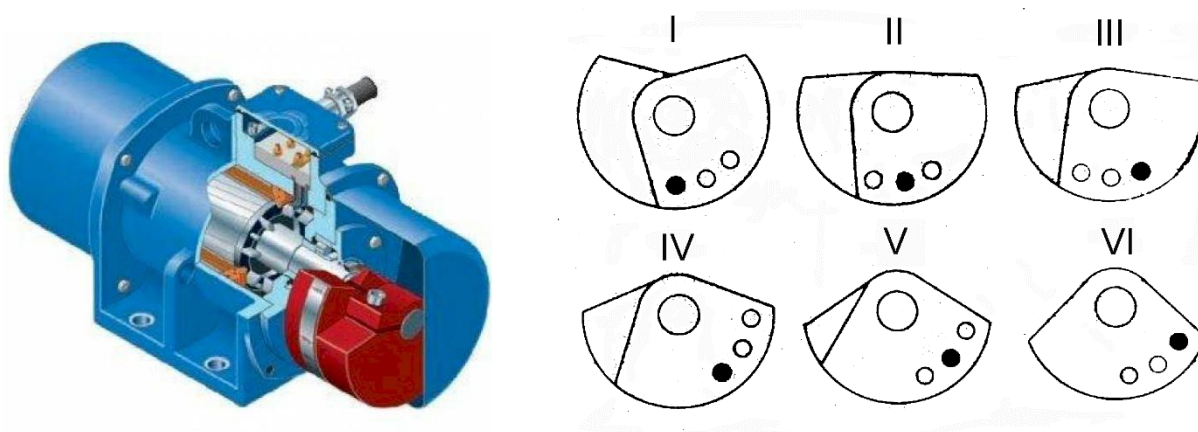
Загальний вигляд та регулювання електромеханічного вібратора
